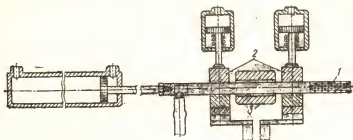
Схема конструкции стержневого индуктора, применяемого в станках-автоматах для закалки отверстий малого диаметра;
